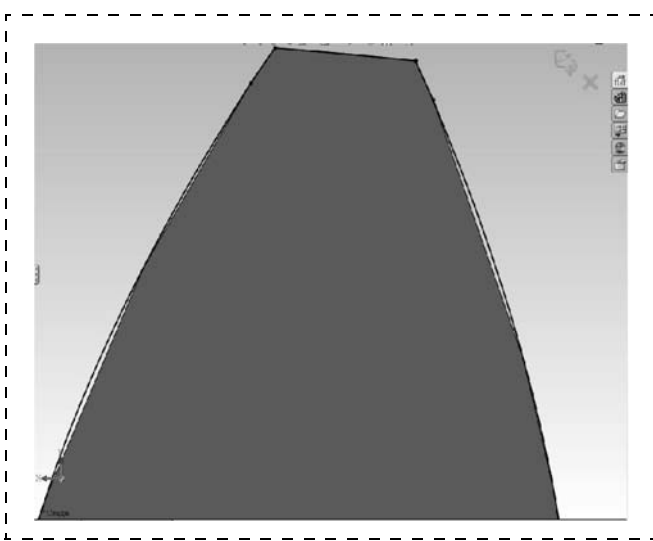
Реальный профиль зуба шестерни, вписанный в идеальный эвольвентный профиль
